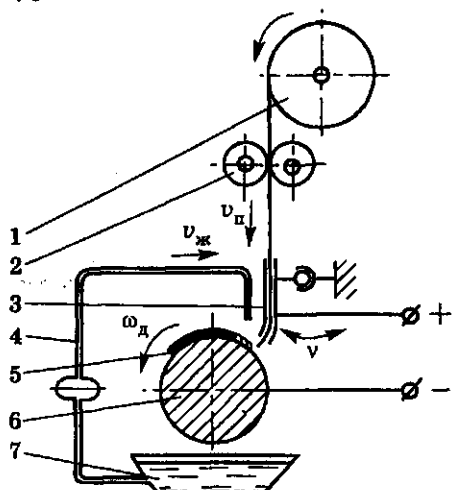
Схема вибродуговой наплавки: 1 — кассета для проволоки; 2 — ролики подающие; 3 — мундштук качающийся; 4 — система подачи раствора; 5 — наплавленный слой; 6 — восстанавливаемая деталь; 7 — емкость; v_n — скорость подачи проволоки; $v_ж$ — скорость подачи раствора; ω_d — угловая частота вращения детали; v — частота качаний мундштука
